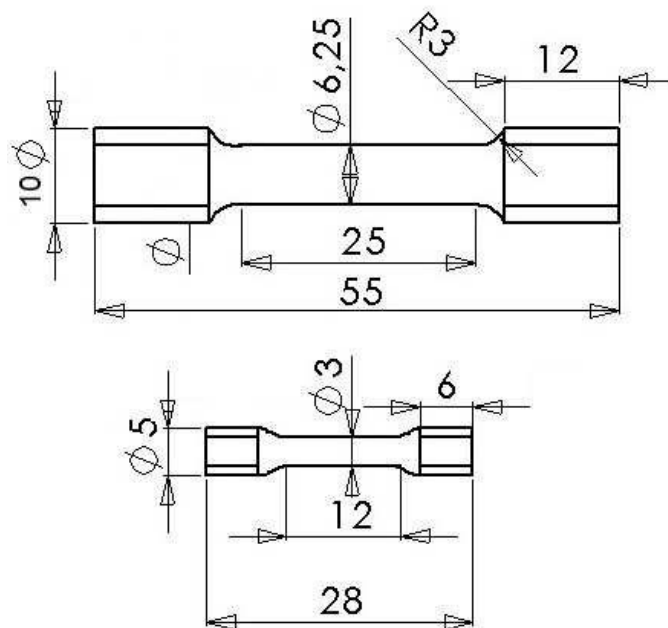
Desenho dos corpos de prova de tração, convencional e de dimensões reduzidas. Dimensões em mm.
